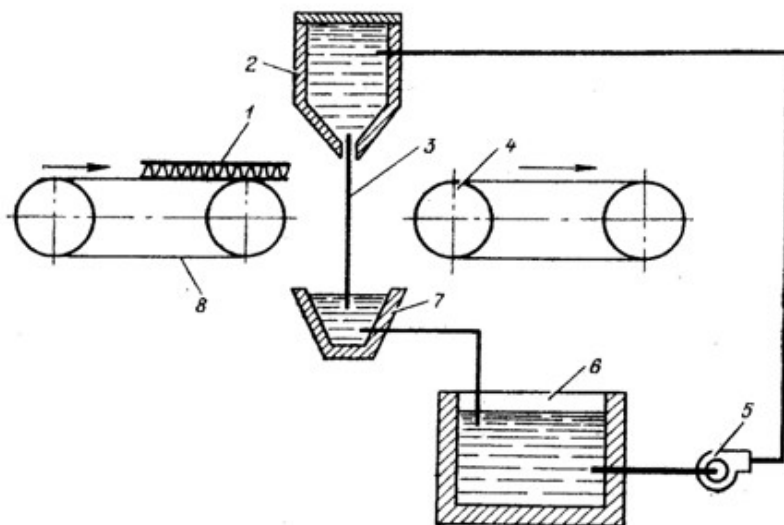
Схема нанесения микровоскового покрытия на заготовки картонных ящиков: 1 – заготовка; 2 – щелевая головка; 3 – завеса; 4 – приемный транспортер; 5 – насос; 6 – расходный бак; 7 – сливной лоток; 8 – подающий транспортер
